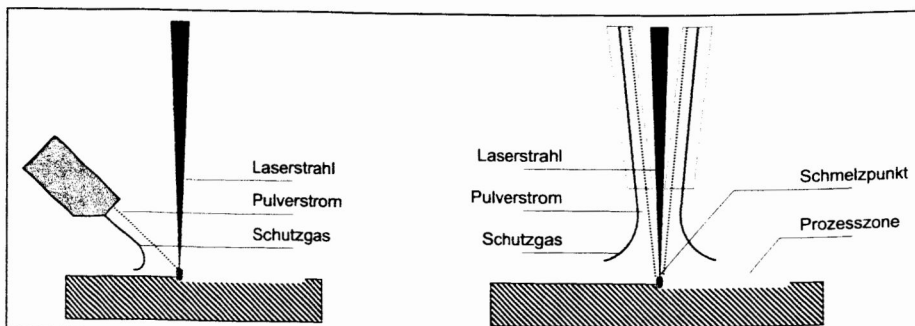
Düsensysteme beim Laserauftragschweißen: off-axis (links) und on-axis (rechts)
